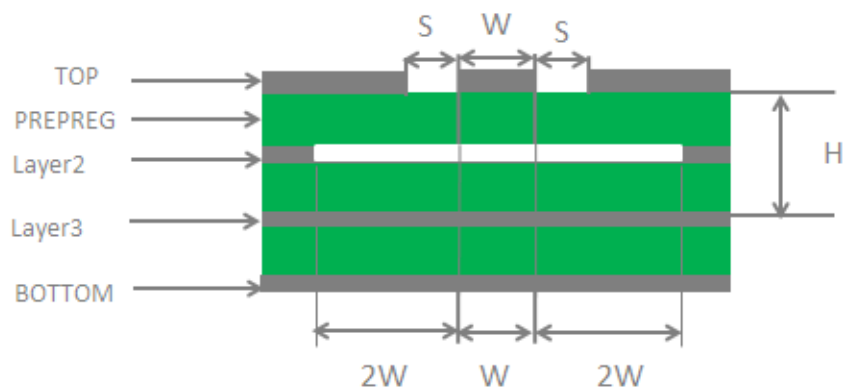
四层 PCB 板共面波导结构 (参考地为第三层)
